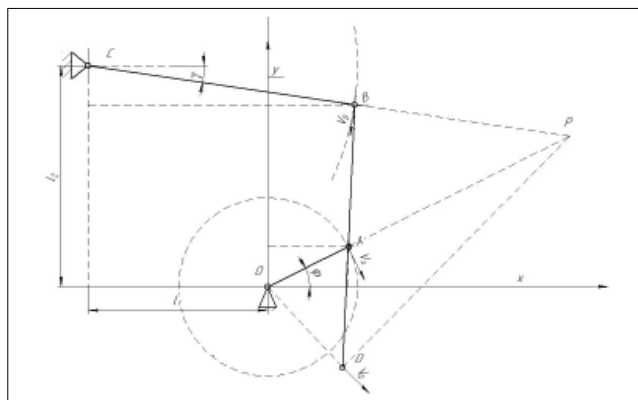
Кинематическая схема очесывающего устройства колебательного типа
